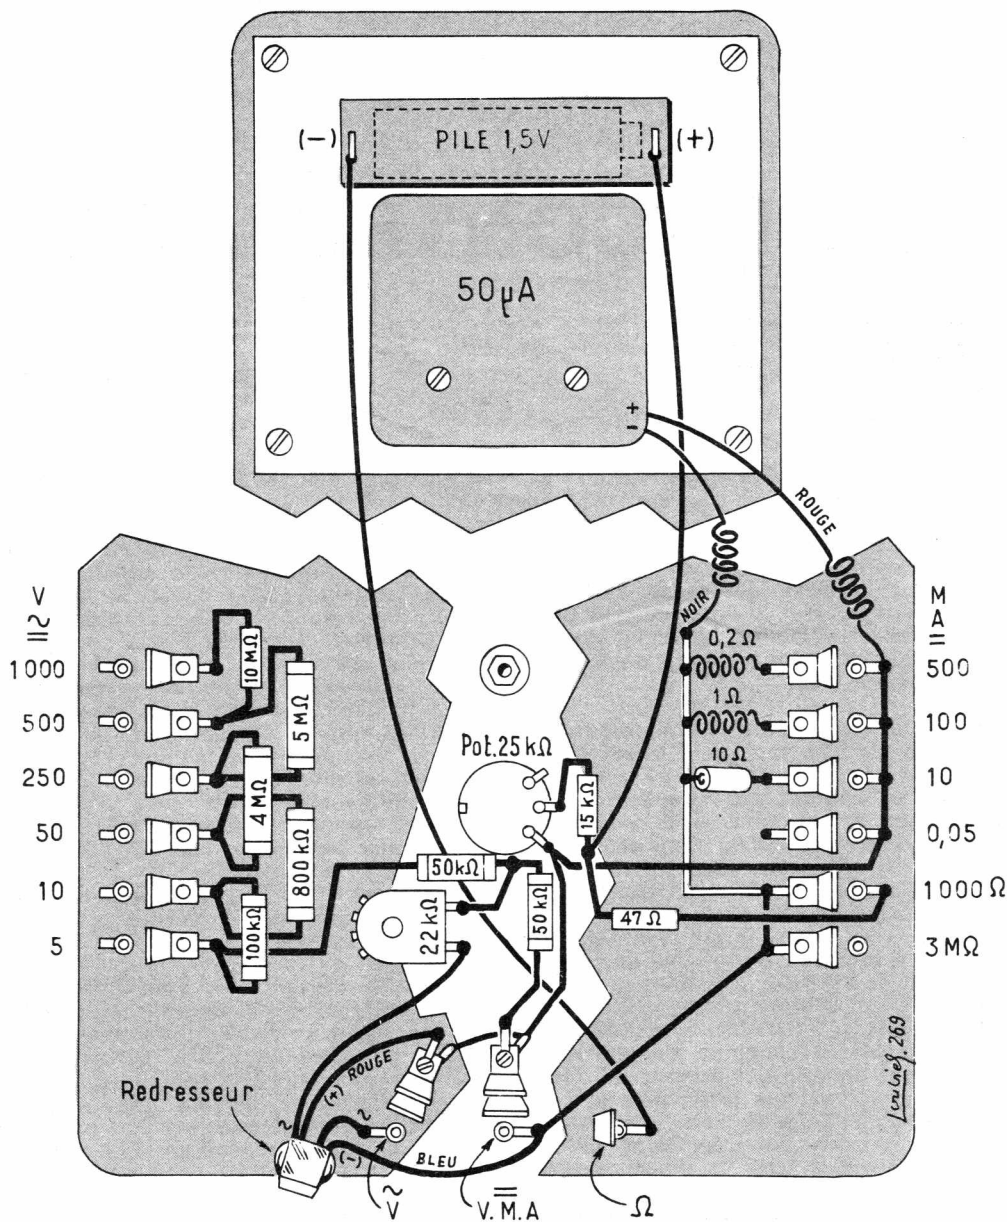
A - PLAN DE CABLAGE EN VUE ÉCLATÉE
